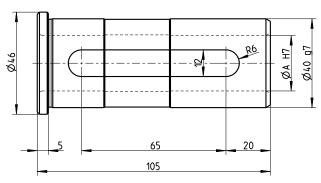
Werkzeughalter für Bohrstangen bis ø40 mm für radial montiertes Dynamometer mit Reduzierhülsen ø40/32 mm, ø40/25 mm, Typ 9129AF40
